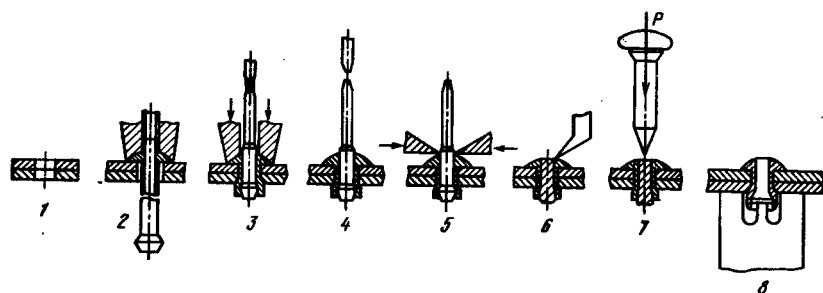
Технологический процесс и контроль установки заклепок с сердечником:
